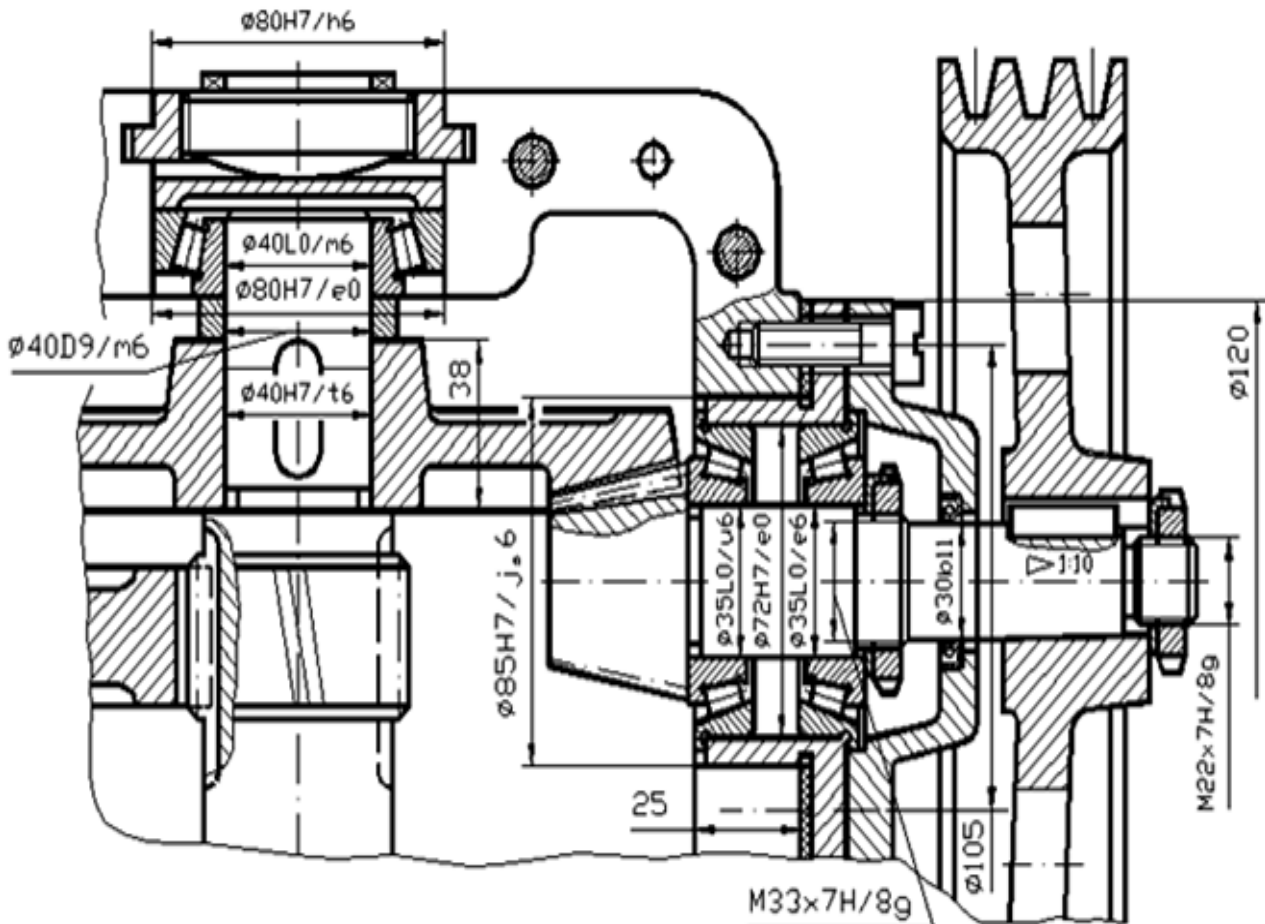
Кресленик конічно-циліндричного редуктора
